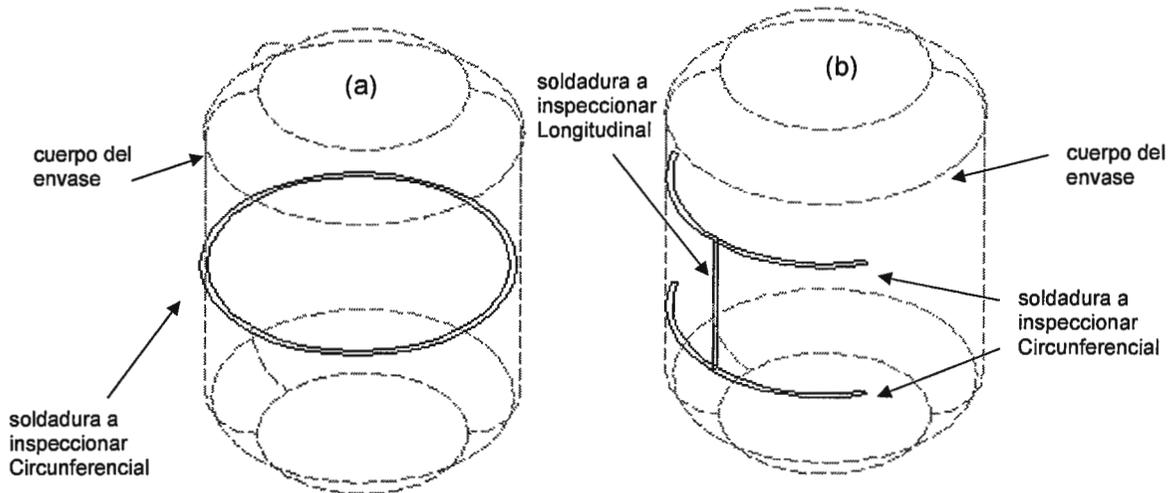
Secciones de la soldadura que se deben de inspeccionar, como mínimo, en los envases clase 3(a) clase 4(b).
